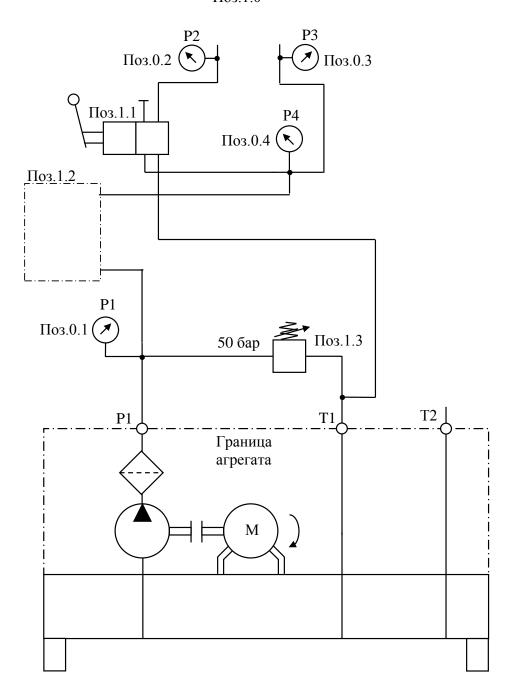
Эскиз гидравлической схемы привода инструмента станка
